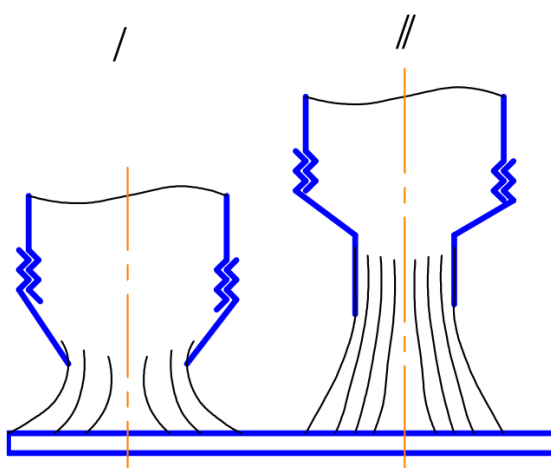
Форма сопел для зварювання в захисних газах
